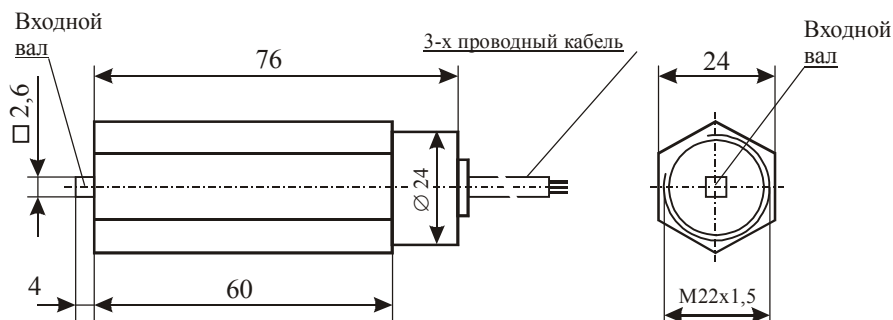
Внешний вид и габаритные размеры датчиков типа СМВ1-Ш24М-12
